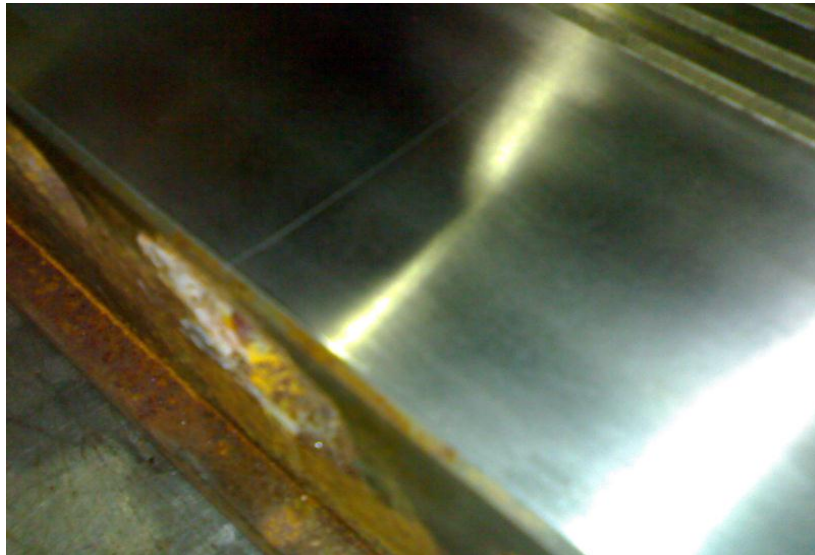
Photo d'un exemple d'incident sur les moules : fissuration
